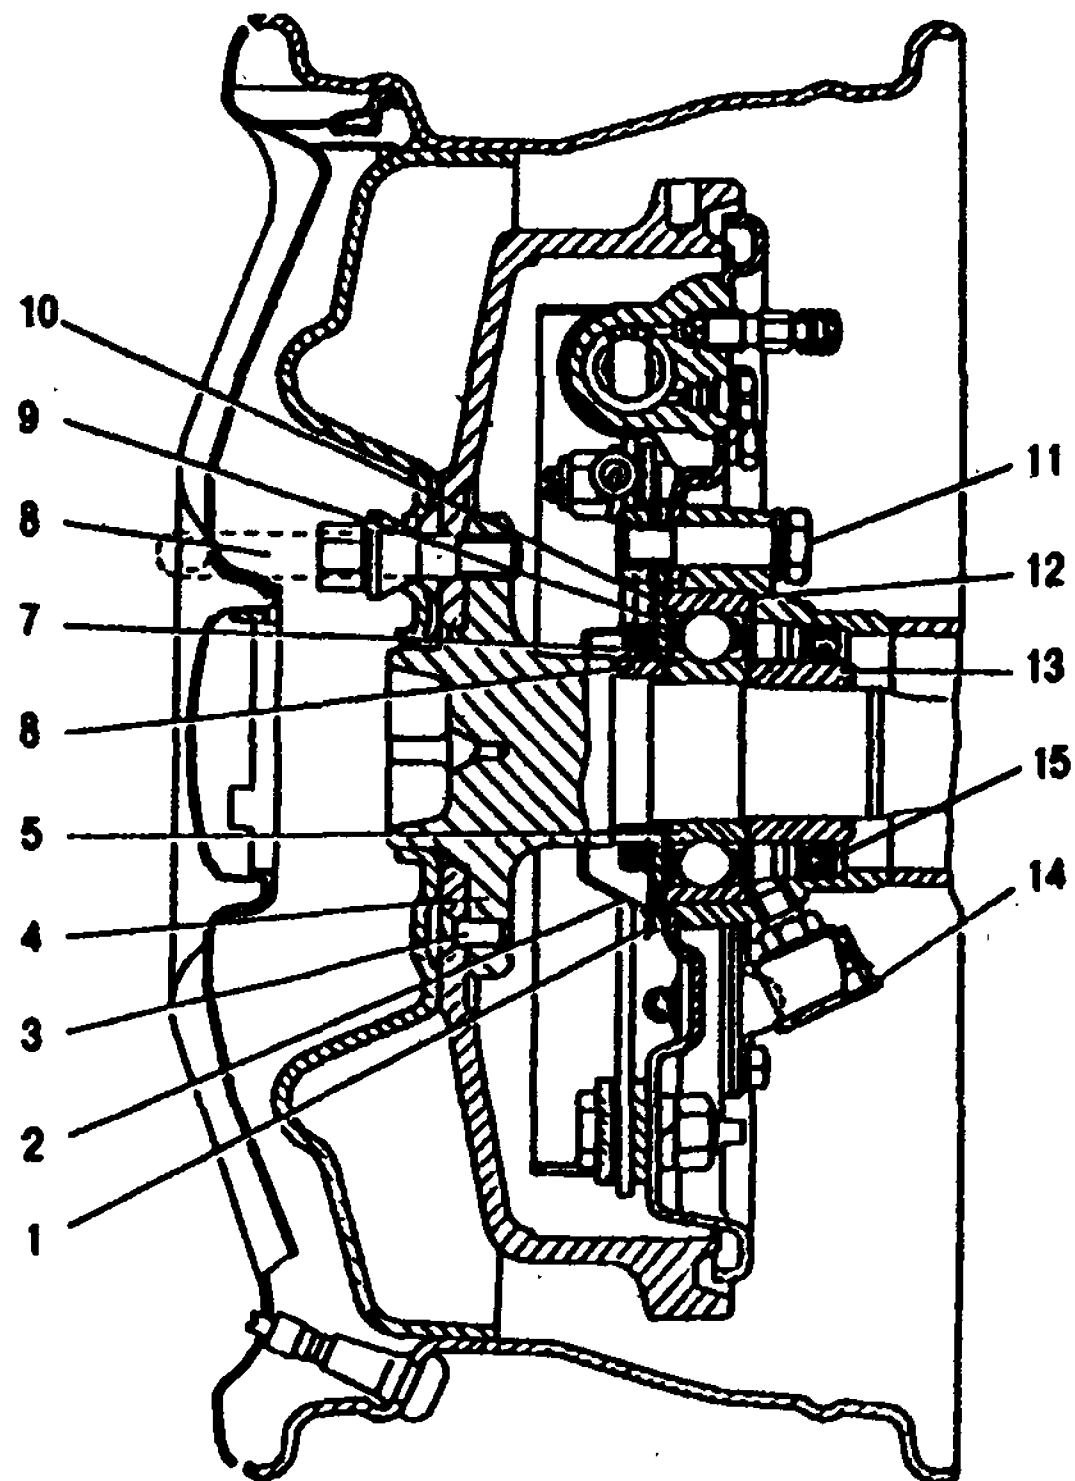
Задний мост (наружная часть): 1 - уплотнительная прокладка между корпусом войлочного сальника и пластиной; 2 - корпус войлочного сальника; 3 - винт крепления тормозного барабана; 4 - полуось; 5 - подшипник полуоси; 6 - втулка; 7 - войлочный уплотнитель; 8 - установочная шпилька (болт крепления колеса); 9 - пластина; 10 - уплотнительная прокладка между пластиной и тормозным щитом; 11 - болт; 12 - пружинное кольцо; 13 - запорная втулка; 14 - колпачковая масленка; 15 - манжета
